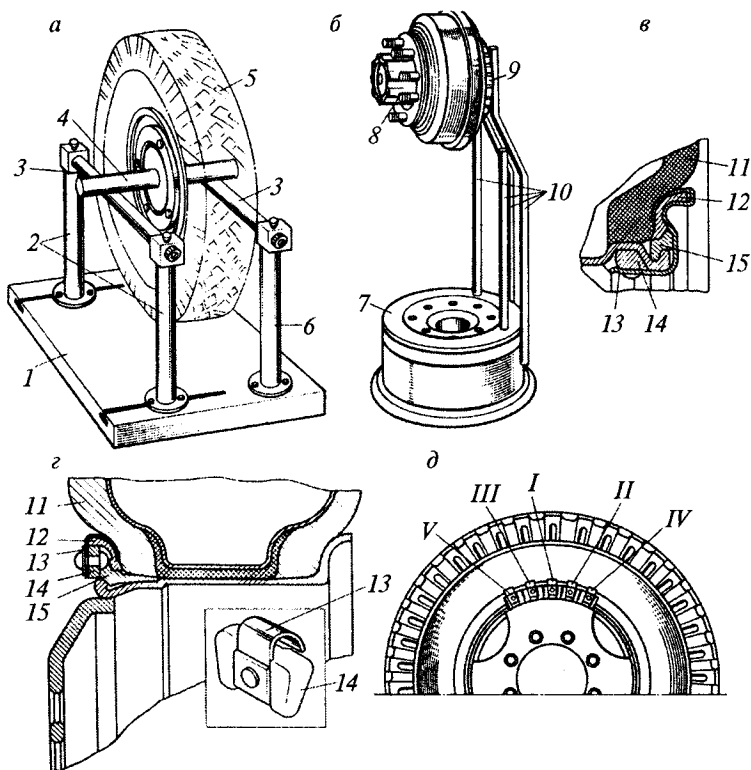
Приспособления для балансировки колес и установка балансировочных грузов
